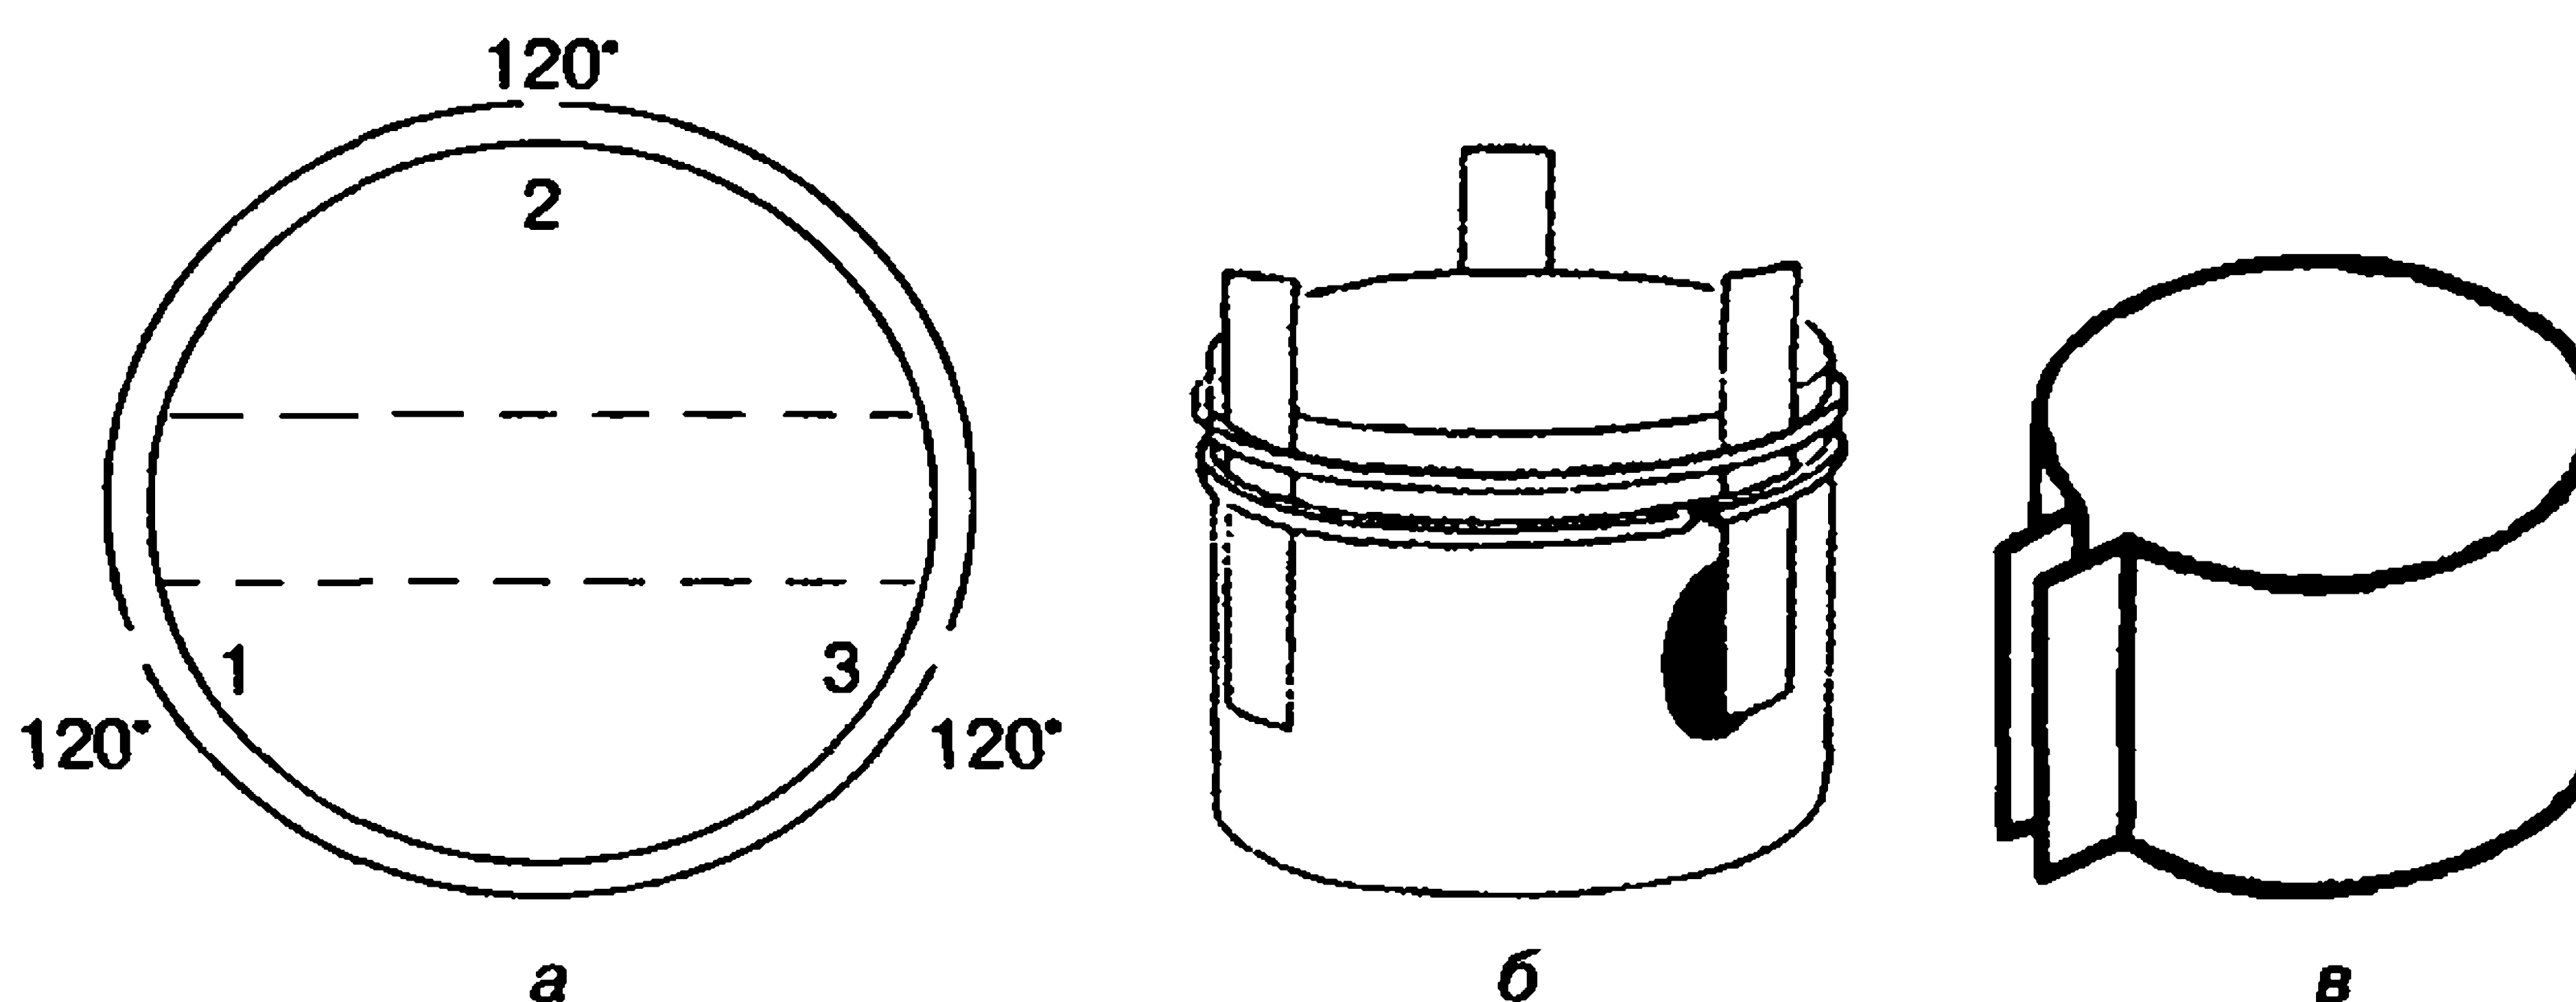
Расположение замков колец (а), жестяные полоски для установки колец (б) и жестяная оправка для сжатия колец на поршне перед установкой в цилиндр (в)
